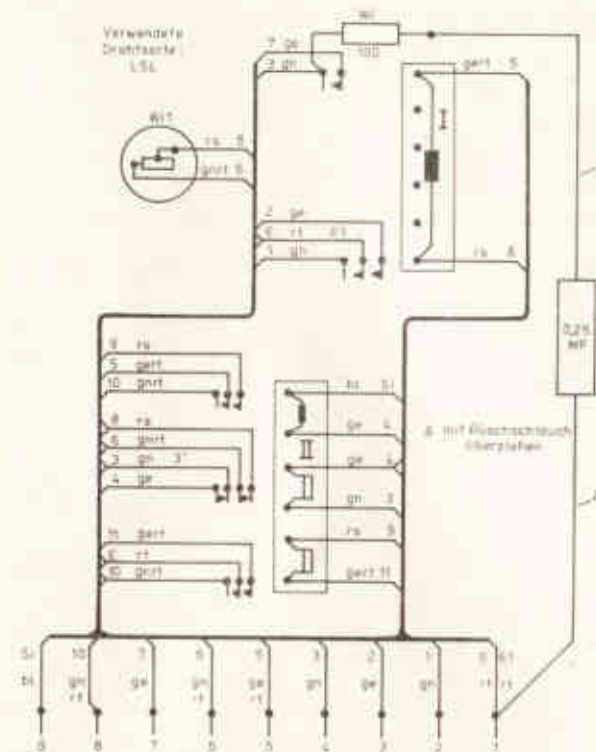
Bauschaltplan, Montageschema (Ms)
